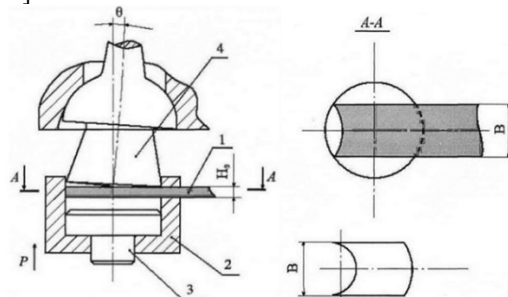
Схема комбінованого процесу рубки і штампування обкочуванням плоских заготовок для виготовлення деталей а); відрубана частина смугової заготовки б) 1 - вихідна заготовка; 2 - матриця; 3 - виштовхувач; 4 - пуансон.
